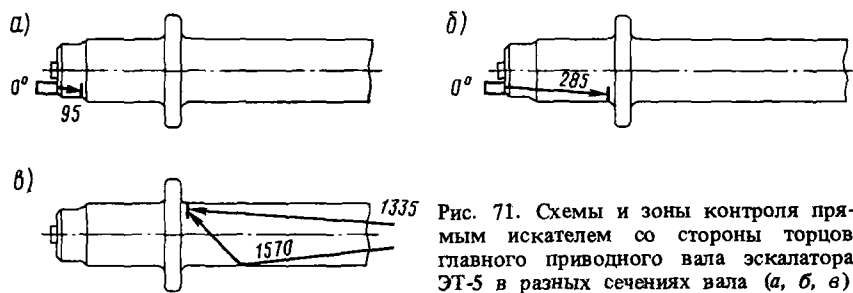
Схемы и зоны контроля прямым искателем со стороны торцов главного приводного вала эскалатора ЭТ-5 в разных сечениях вала (а, б, в)
